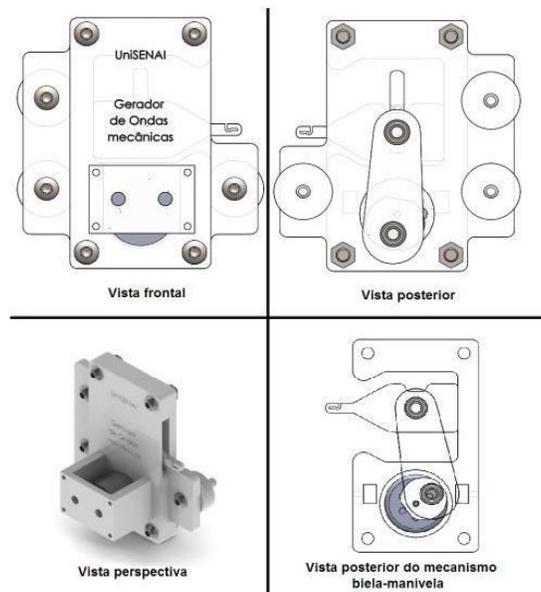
Representação do conjunto do gerador de ondas mecânicas
